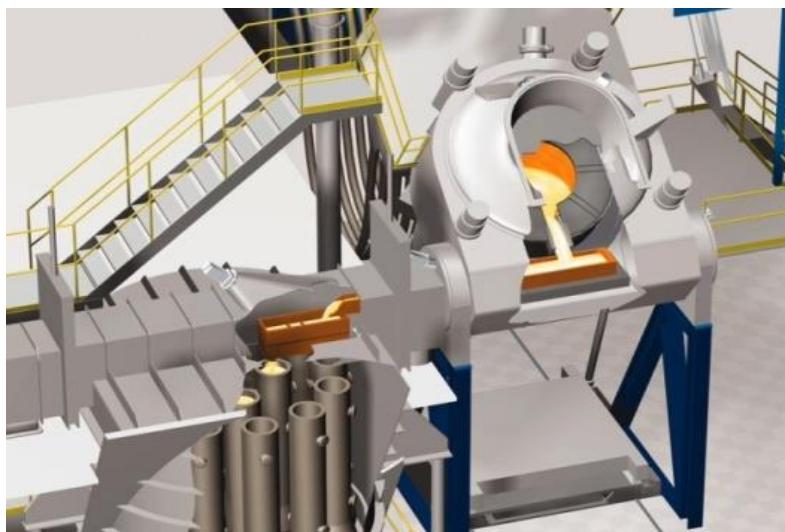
Установка для вакуумной индукционной плавки и заливки металла ВИДП
